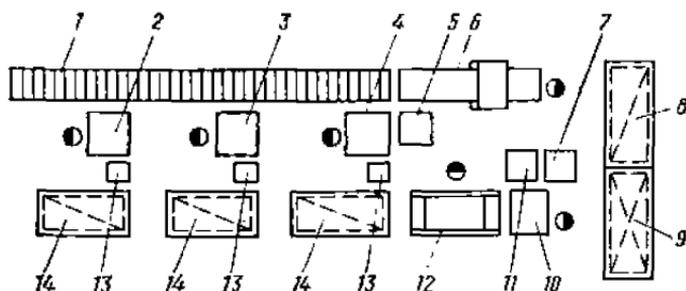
Схема расположения оборудования на поточно-механизированной линии изготовления двусторонних мягких элементов на базе блоков из губчатой резины:
